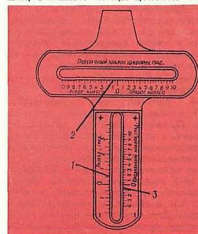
Шкалы прибора для проверки развала колес: 1 — шкалы развала колес; 2 — шкала поперечного наклона шкворня; 3 — шкала продольного наклона шкворня.
